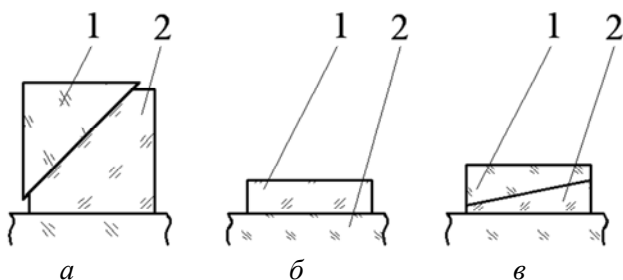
Закрепление заготовок действием сил молекулярного сцепления:
